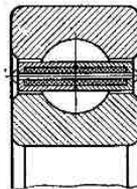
Шарикоподшипник, а сепаратор которого запрессован в твердый смазочный материал
